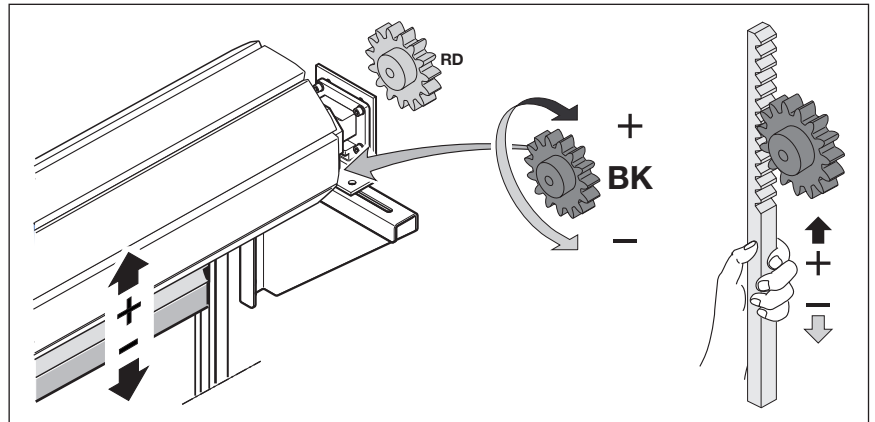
Винт с рифленной головкой ВК для конечного положения *Ворота Откр.*, приспособление для регулировки
